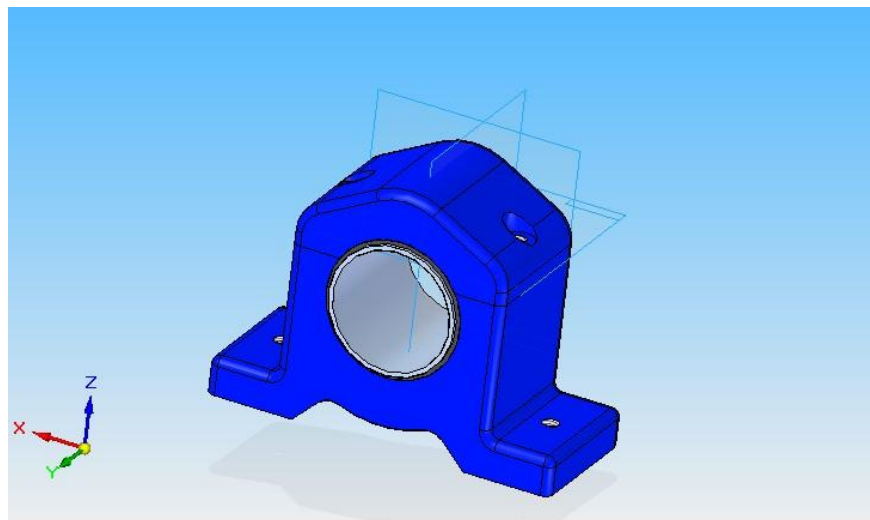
Dibujo del soporte para rodamientos de tipo pie SAF
